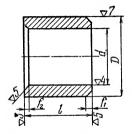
Втулка для восстановления изношенного отверстия под подшипник вала муфты сцепления.
